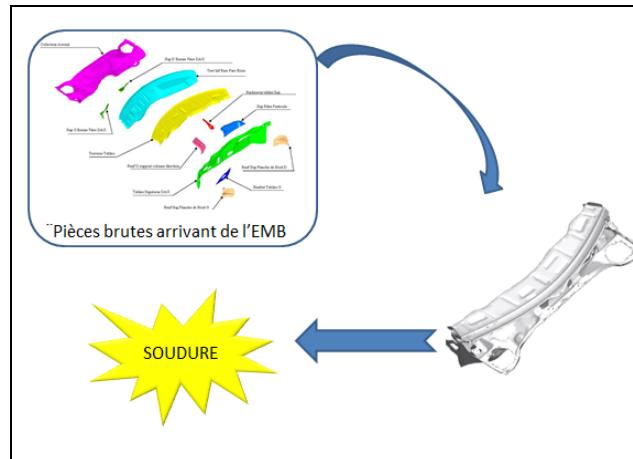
Principe d'un assemblage soudé au ferrage (source interne : Doc info)
